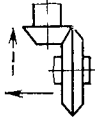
Нулевое положение ведущей шестерни и направление ее сдвига
